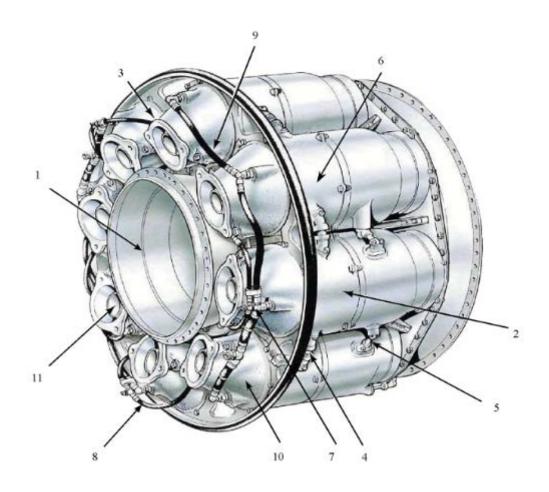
Трубчатая КС: *1* – внутренний корпус двигателя; *2* – корпус; *3* – фланец соединения с компрессором; *4* – пламеперебрасывающая муфта; *5* – дренажная труба; *6* – противопожарная перегородка; *7* – форсунка; *8* – коллектор первого контура; *9* – коллектор второго контура; *10* – диффузор; *11* – заборник первичного воздуха
